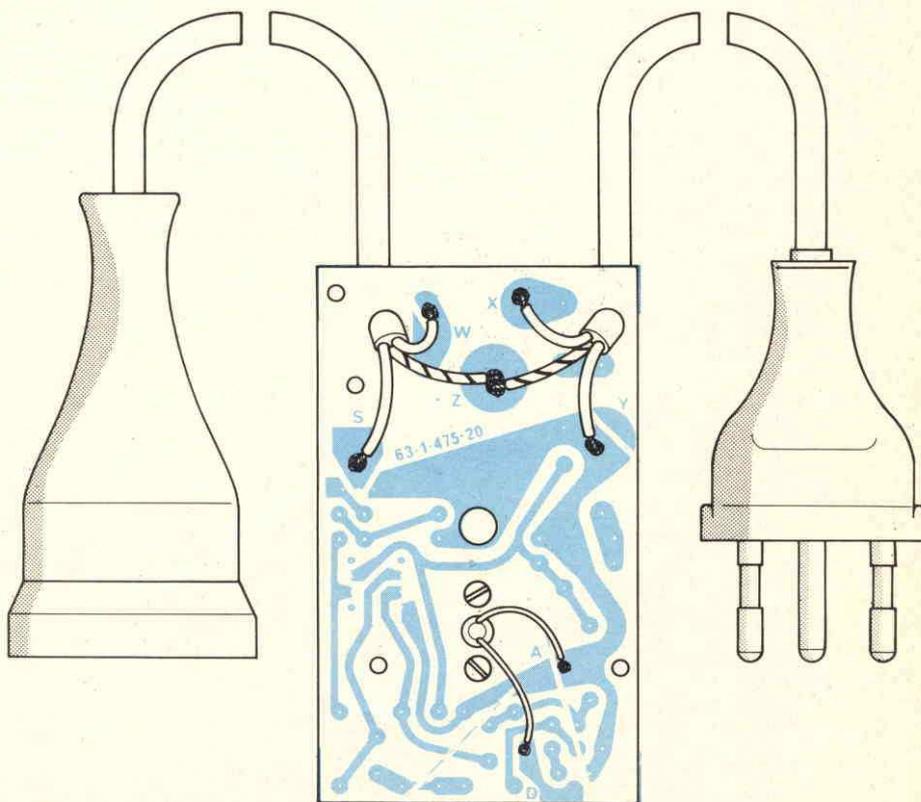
Cablaggio del Kit Amtron UK 726.
